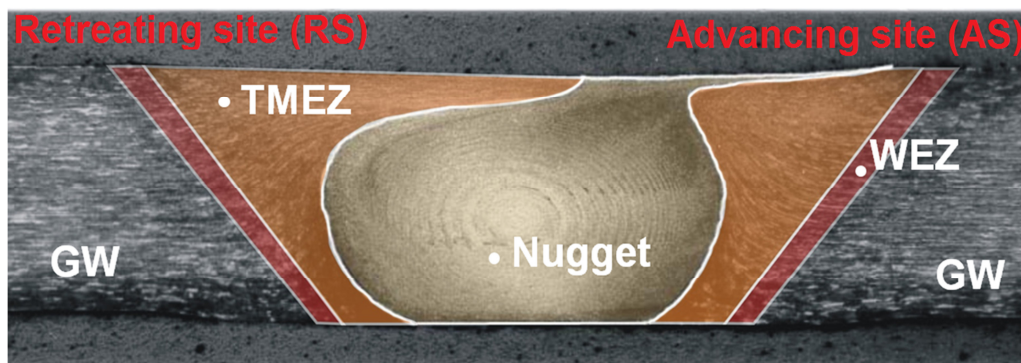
Mikrostruktur der Rührreißschweißverbindung
